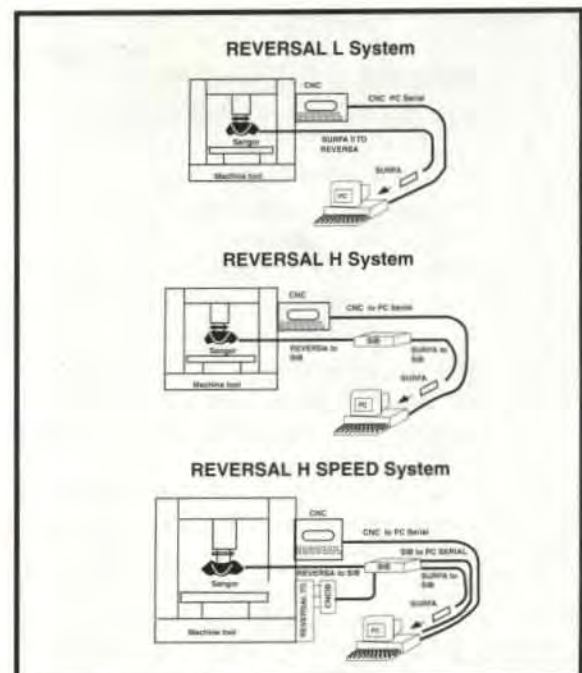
Cabezal láser montado en una máquina herramienta C.N.C.
